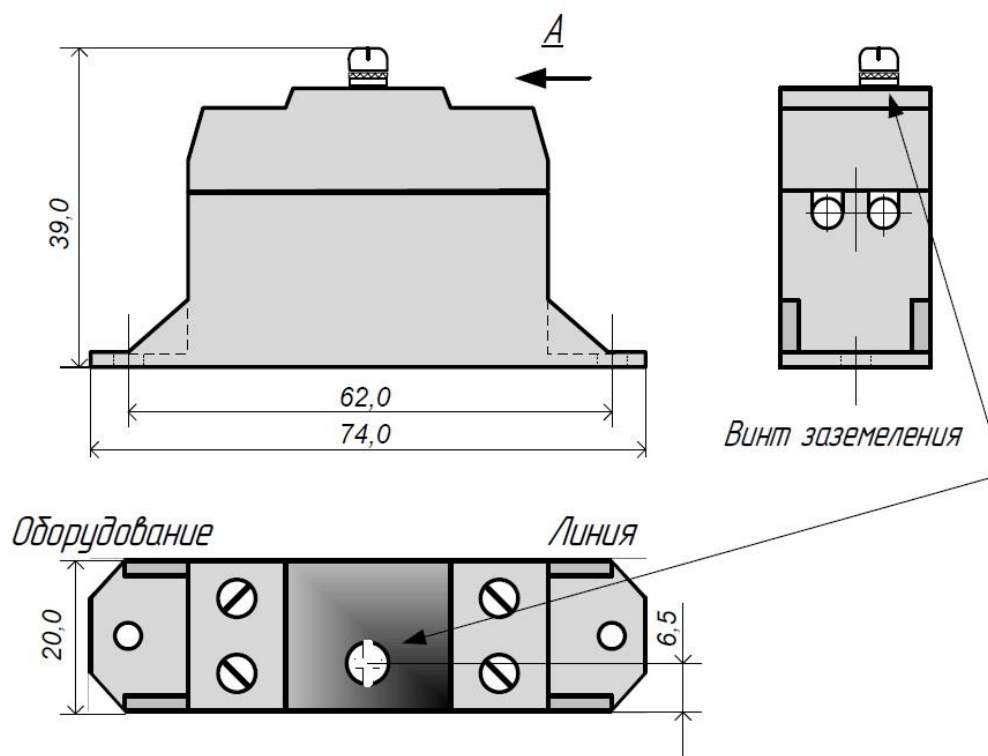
Габаритные размеры устройства Commeng Hard DIP
